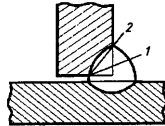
Схема расчетных сечений сварного соединения с угловым швом:
